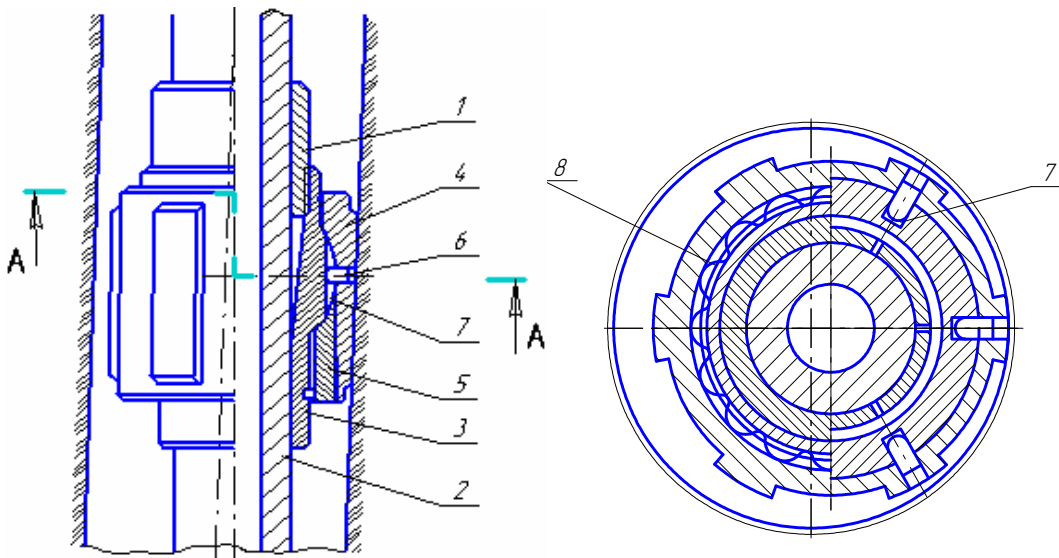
Принципова схема конструкції пересувного шарнірного ОЦЕ
